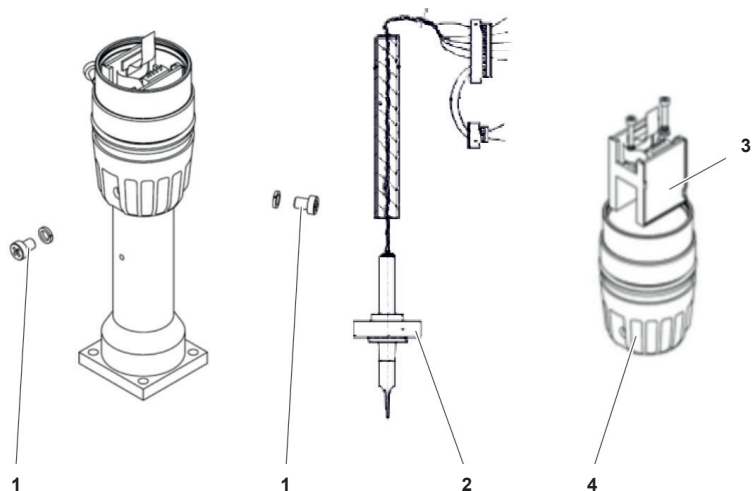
Skříň převodníku, integrální konstrukce průtokoměru
